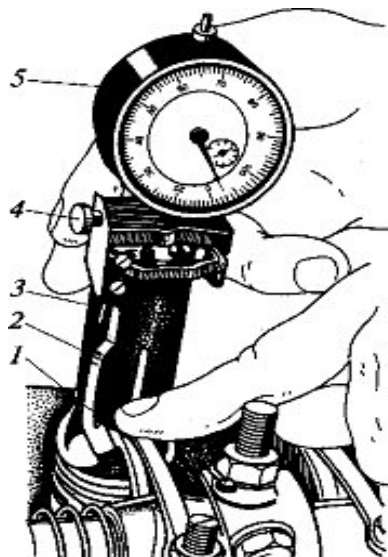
Визначення теплового зазору приладом КИ-9918 (1-коромисло; 2-рухома каретка; 3-корпус; 4-стопорний гвинт; 5-індикатор)
